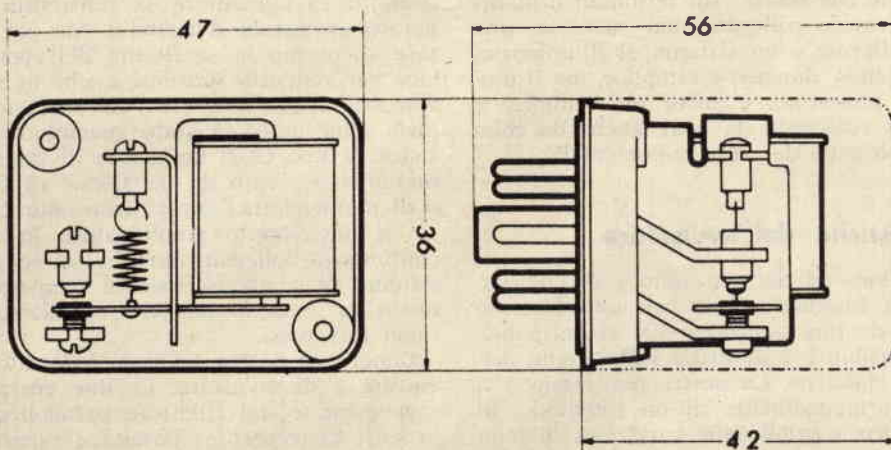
Schema elettromeccanico del relè Ducati 51.10.03 con dimensioni principali espresse in mm.
